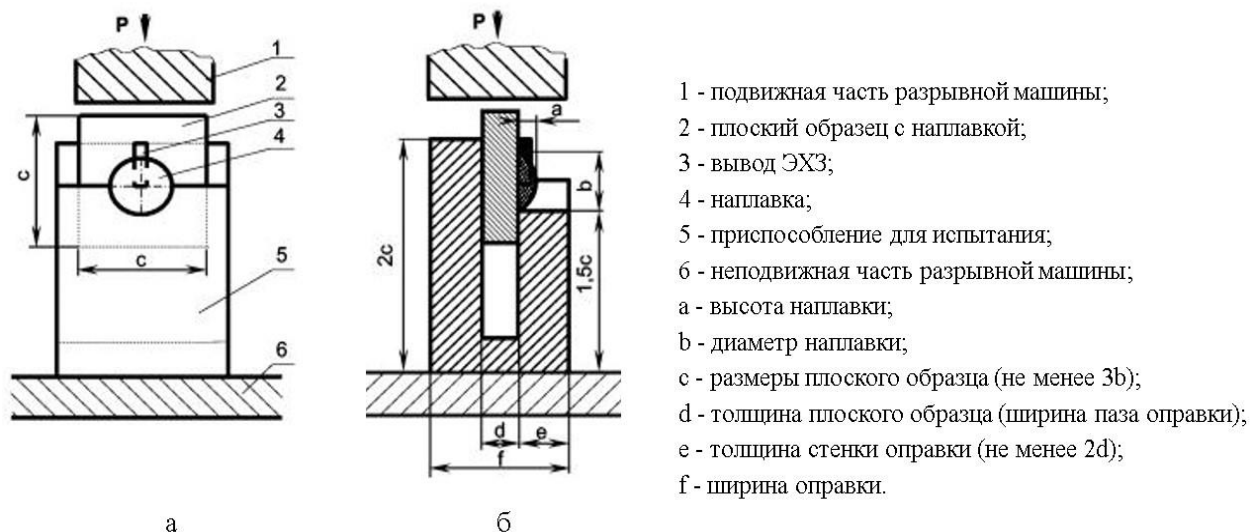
Схема механических испытаний на сдвиг наплавки вывода ЭХЗ, выполненной термитной сваркой: а – вид спереди, б – вид сбоку
